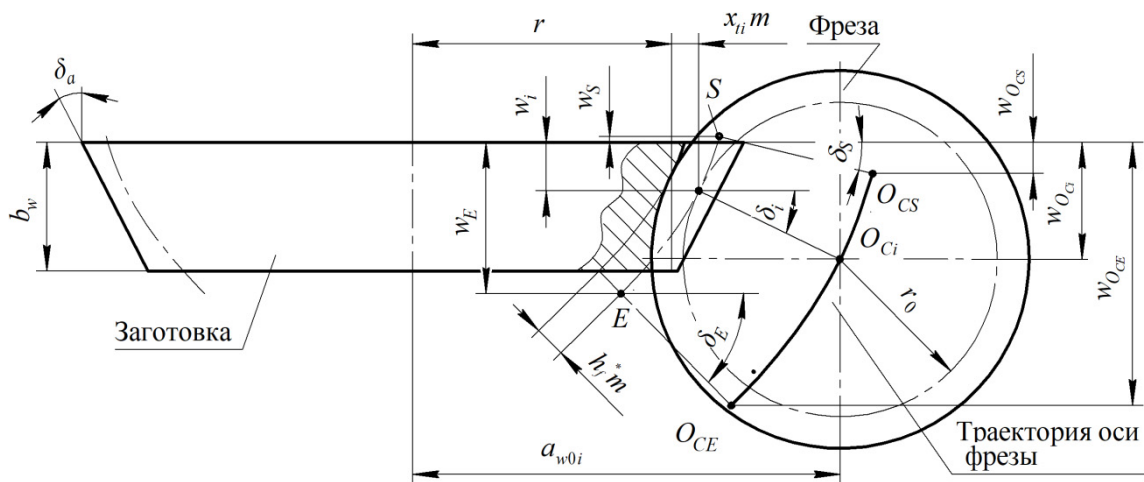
Схема станочного зацепления заготовки шестерни и фрезы
